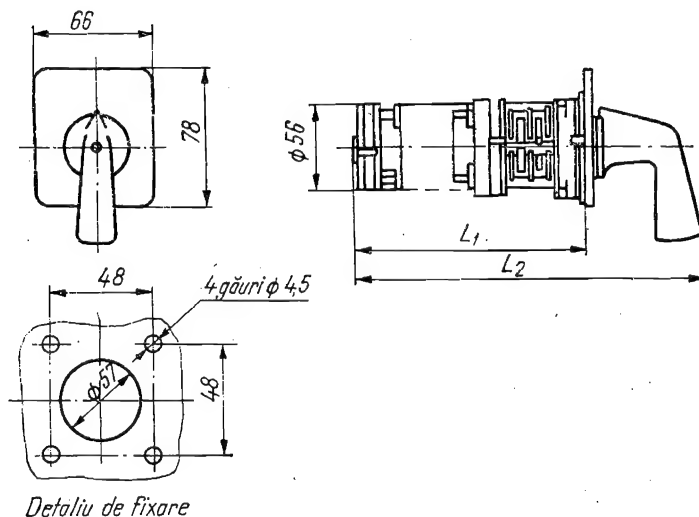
Dimensiuni de gabarit și montaj ale tipului de comutator C. 16 cu revenire.
